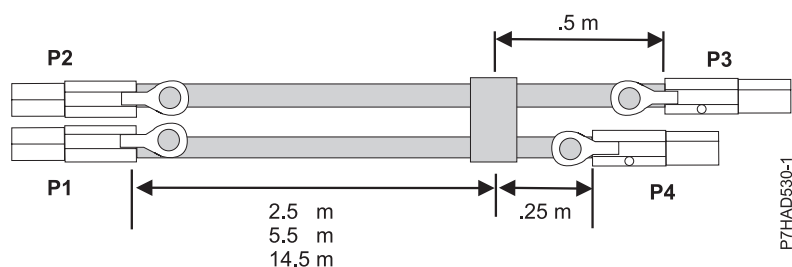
Comprimentos de cabos de montagem de cabo X externo SAS
